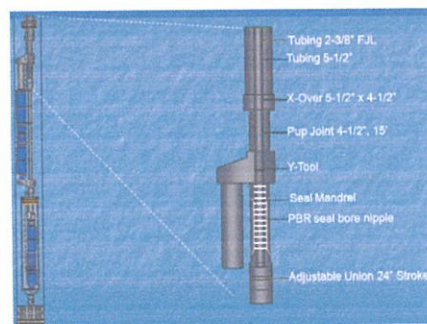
Partes que constituyen la Y-Tool. i-Handbook.exe Schlumberger. Septiembre 2009
